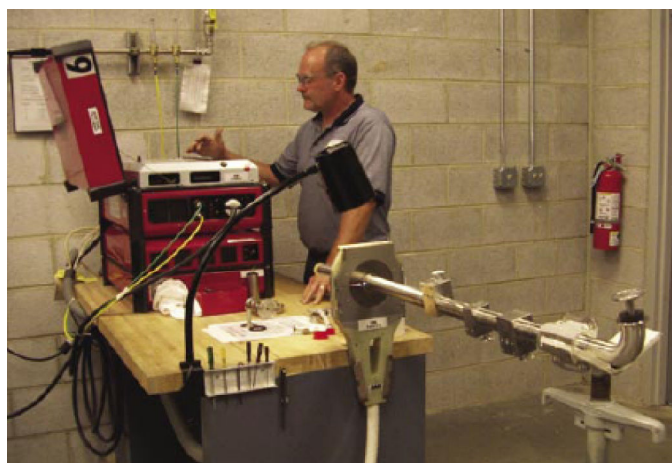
Soldadura Orbital en Tubería. (Fotografía por Arc Machines Inc.)
